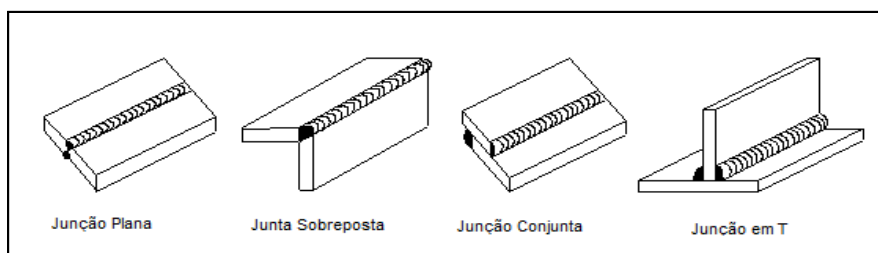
Tipos de junta na soldagem eletrodo revestido
